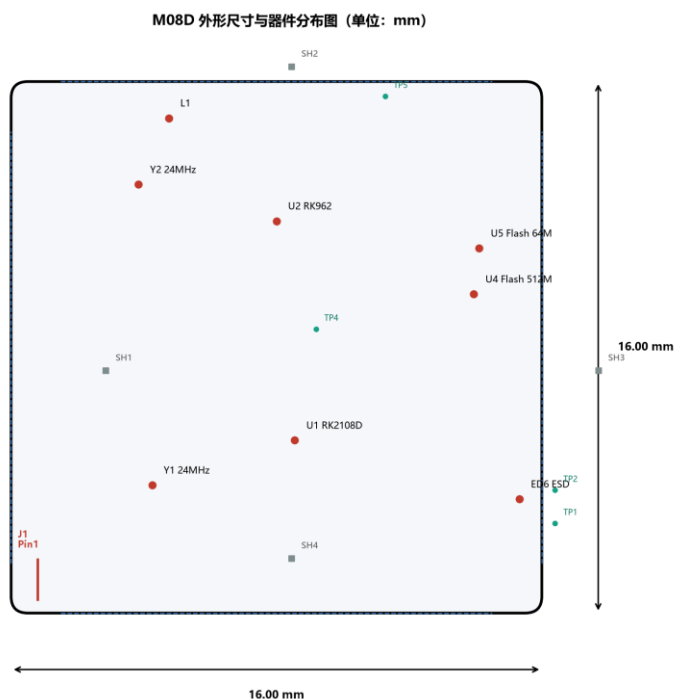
M08D 外形尺寸图 (2D Mechanical Drawing, mm)
